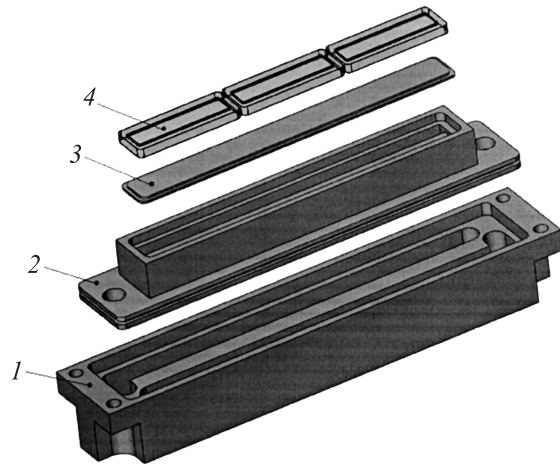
Сборка из матриц лазерных диодов СЛМ-3: 1 — корпус, 2 — радиатор, 3 — крышка радиатора, 4 — матрица лазерных диодов.
